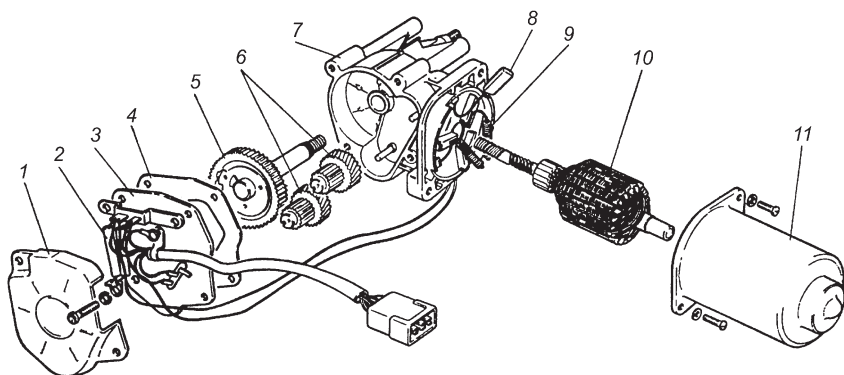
Детали моторредуктора очистителя ветрового стекла:
